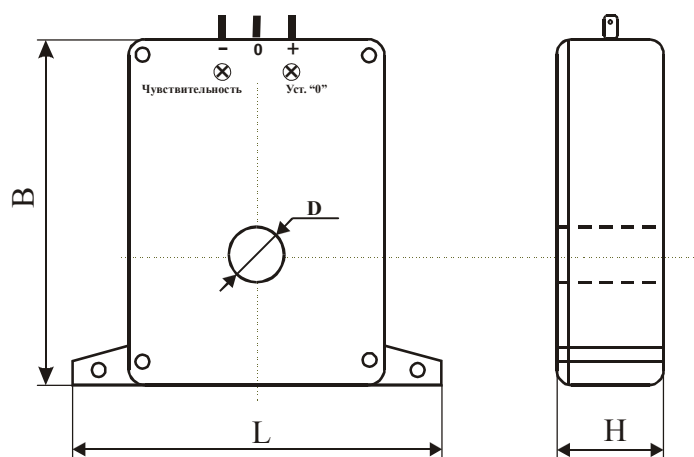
Внешний вид и габаритные размеры датчиков тока серий CSLE и CSLF, размещенных в пластмассовом корпусе
